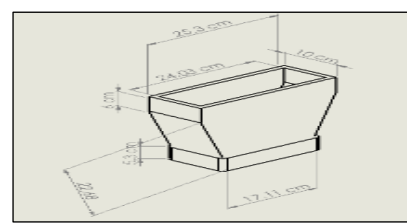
Plano Pieza 3: dispensador de Jabón. Fuente:
